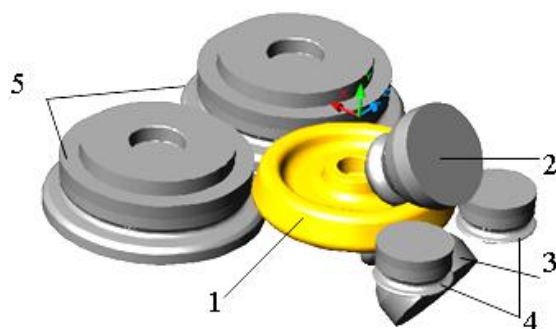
Схема расположения валков и заготовки в начальный момент прокатки: 1 – заготовка, 2 – верхний наклонный валок, 3 – нижний наклонный валок, 4 – нажимной валок, 5 – коренной валок.
